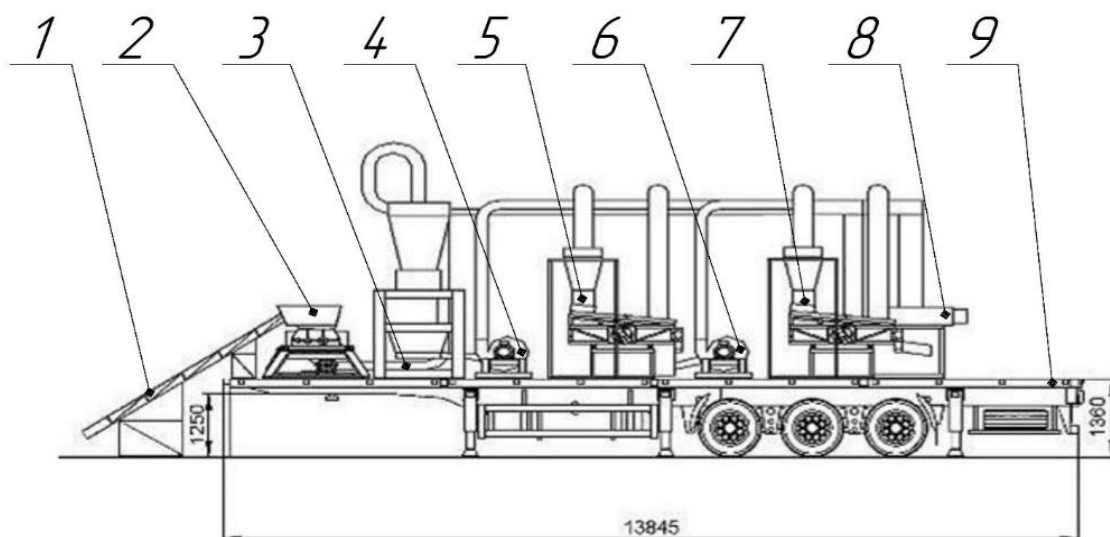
Оборудование мобильного комплекса: 1 – Транспортер; 2 – шредер; 3 – дефибратор металлического корда; 4 – первая роторная дробилка; 5 – первое вибросито; 6 – вторая роторная дробилка; 7 – второе вибросито; 8 – вентилятор высокого давления; 9 – контейнерная платформа
